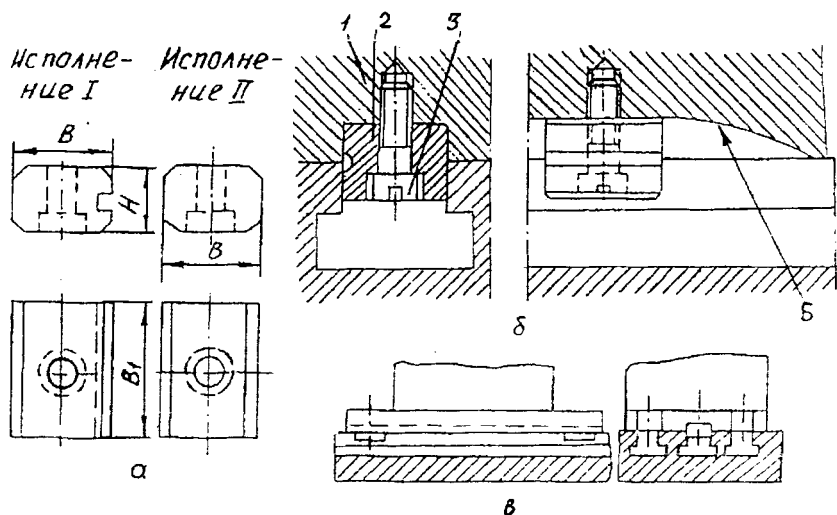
Установка приспособлений с помощью шпонок на фрезерных станках: а — конструкции стандартных шпонок; б — способ крепления шпонок на приспособлении; в — схема установки
